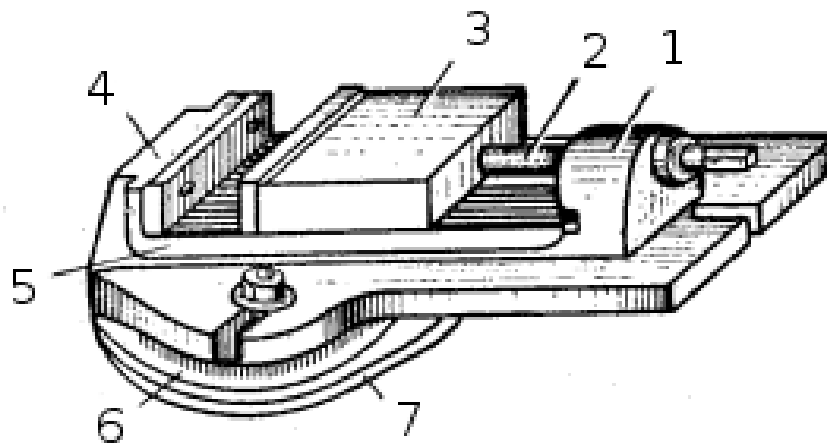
Поворотные машинные тиски: 1 — кронштейн; 2 — винт; 3 — подвижная губка; 4 — неподвижная губка; 5 — корпус; 6 — градусная шкала; 7 — нижняя плита.
